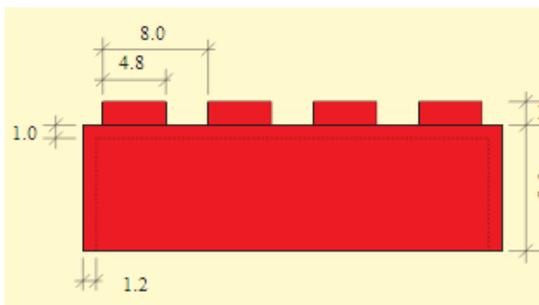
Vista lateral izquierda de una pieza de LEGO 4 x 2, [6]
